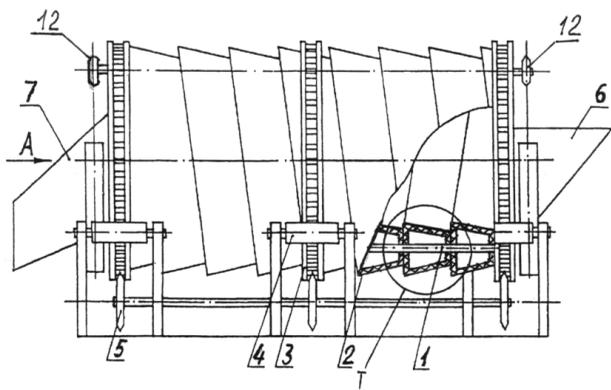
Общий вид устройства для очистки корнеплодов (вид сбоку)
